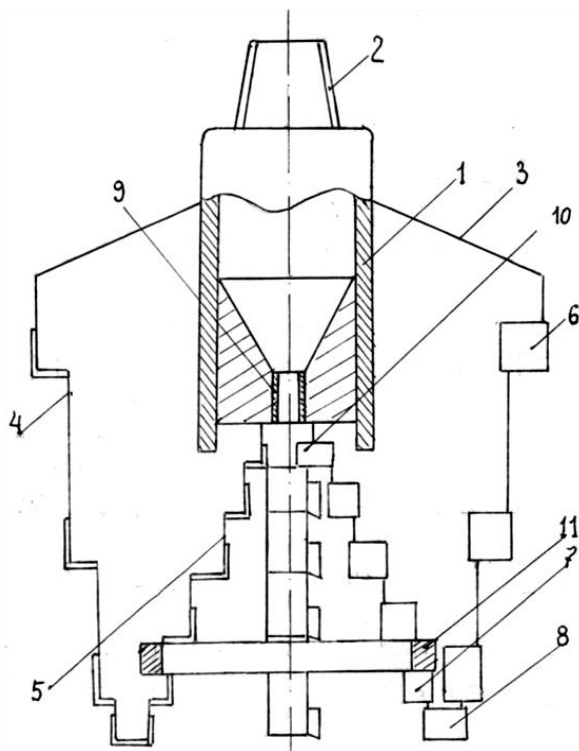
Буровое долото типа пикобур (патент РК №33077 (104033)): 1 – корпус; 2 – резьба; 3 – лопасть; 4 – уступ наружный; 5 – уступ внутренний; 6 – резец наружного уступа; 7 – резец внутреннего уступа; 8 – резец врубовой; 9 – гидронасадка; 10 – кернолом; 11 – кольцо жесткости
